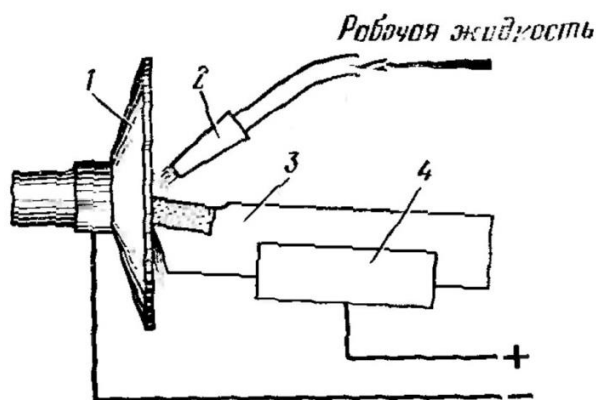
Схема анодно-механічної заточки інструменту.
